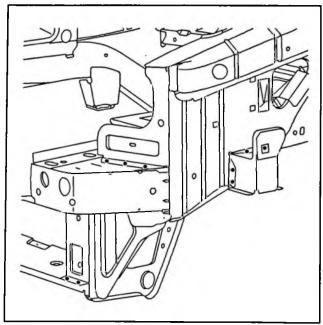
AP02RC Souder par points électriques. Souder par points "bouchon" MAG.
